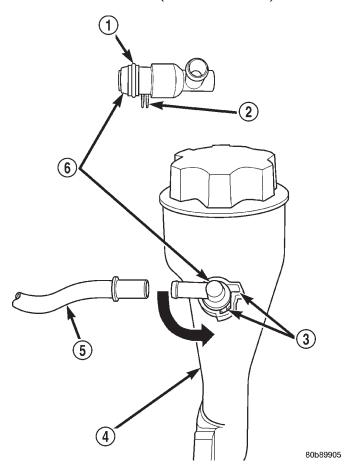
Localización de la válvula PCV y tubo de llenado de aceite
